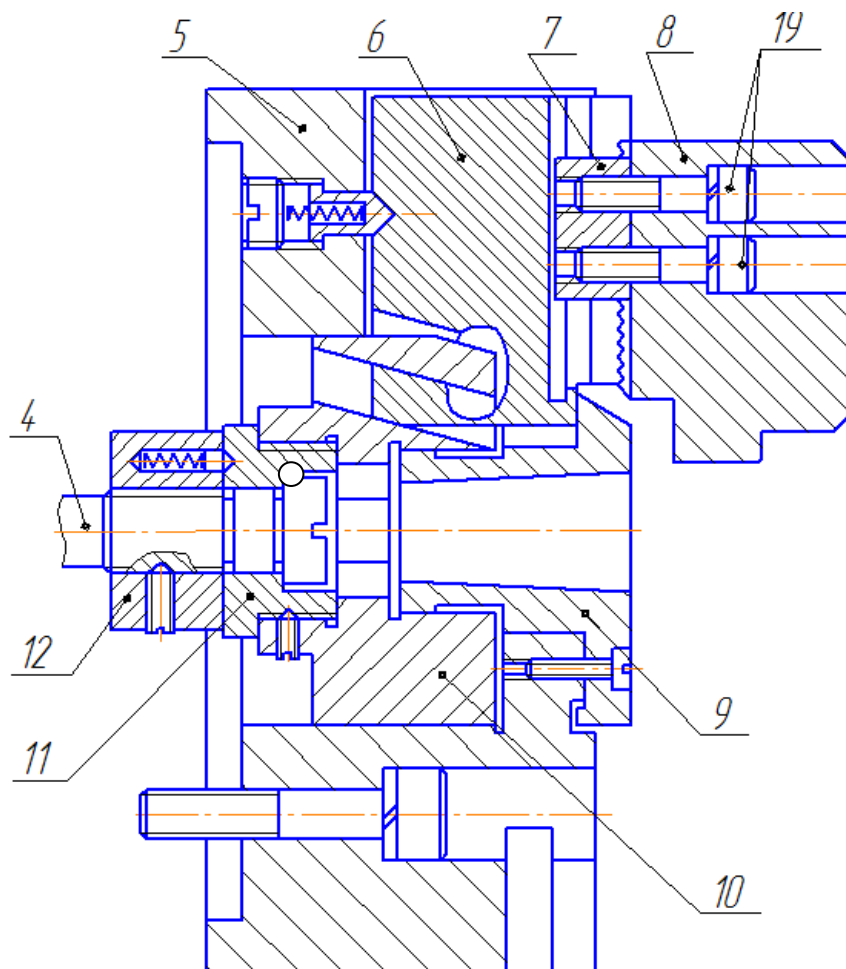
Токарный трёхкулачковый самоцентрирующийся клиновой патрон;
